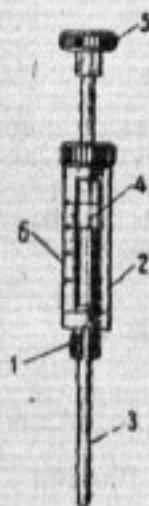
Индикатор Фиат для определения положения поршня: 1 — наконечник с резьбой для установки индикатора; 2 — корпус индикатора в виде трубы с прорезью; 3 — стержень; 4 — ползун; 5 — верхняя головка для установки на «0»; 6 — шкала
